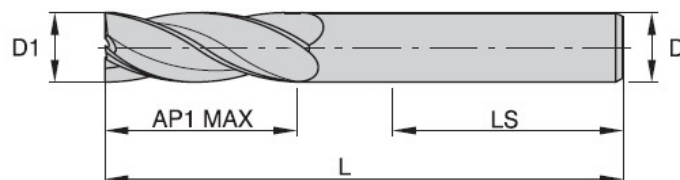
Fréza F3AH1800ADL30 [7]
